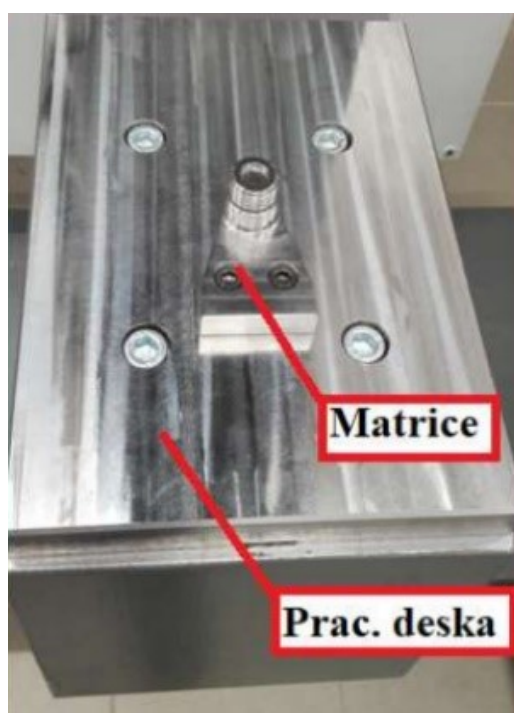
Nýtovací zařízení pro metodu self-rivet piercing
